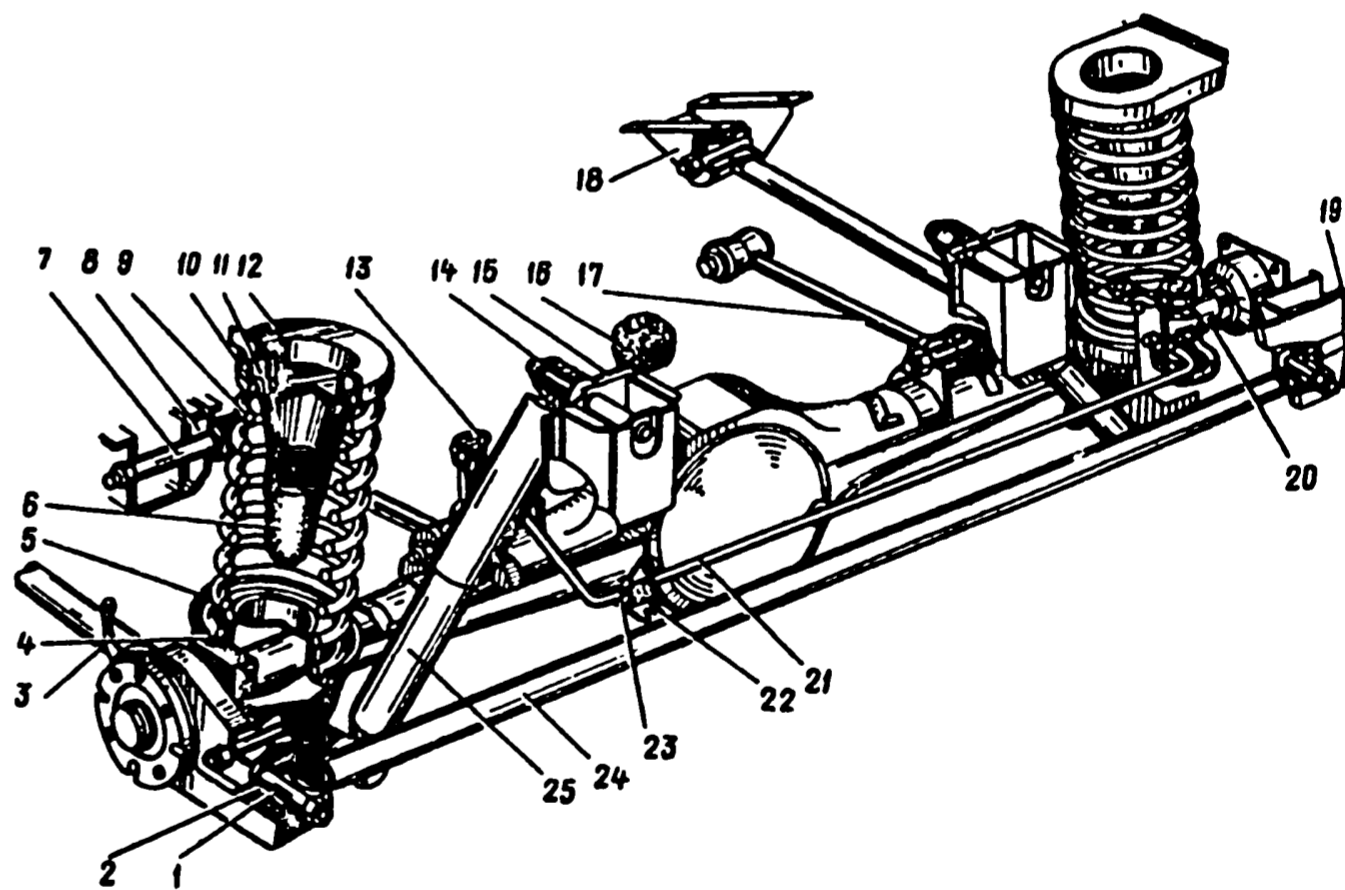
Задняя подвеска: 1 - распорная втулка; 2 - резиновая втулка; 3 - нижняя продольная штанга; 4 - нижняя изолирующая прокладка пружины; 5 - нижняя опорная чашка пружины; 6 - буфер хода сжатия; 7 - болт крепления верхней продольной штанги; 8 - кронштейн крепления верхней продольной штанги; 9 - пружина подвески; 10 - верхняя чашка пружины; 11 - верхняя изолирующая прокладка пружины; 12 - опорная чашка пружины; 13 - тяга рычага привода регулятора давления задних тормозов; 14 - резиновая втулка проушины амортизатора; 15 - кронштейн крепления амортизатора; 16 - дополнительный буфер хода сжатия; 17 - верхняя продольная штанга; 18 - кронштейн крепления нижней продольной штанги; 19 - кронштейн крепления поперечной штанги к кузову; 20 - регулятор давления задних тормозов; 21 - рычаг привода регулятора давления; 22 - обойма опорной втулки рычага; 23 - опорная втулка рычага; 24 - поперечная штанга; 25 - амортизатор
